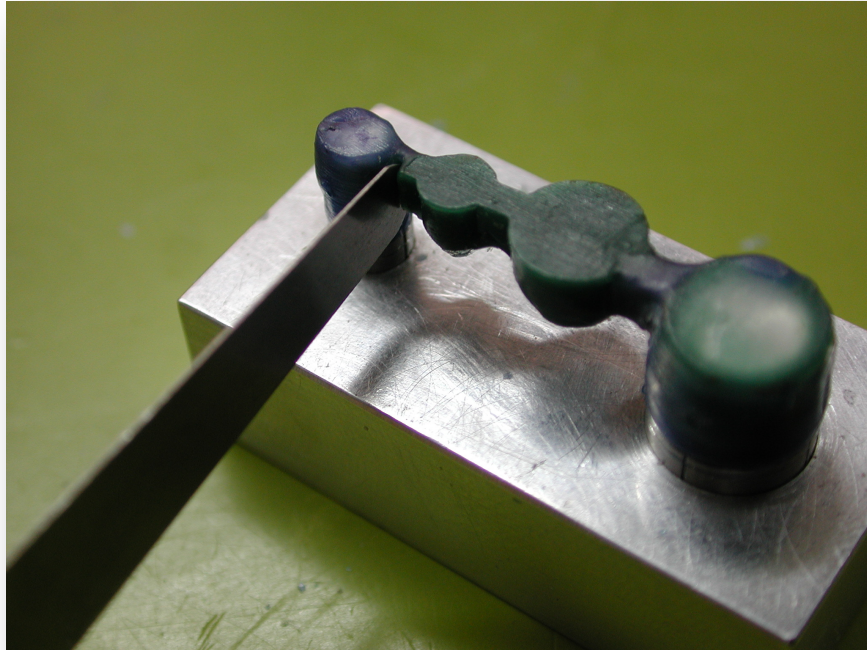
Tanza de 0,13 mm usada para separar las partes a soldar
